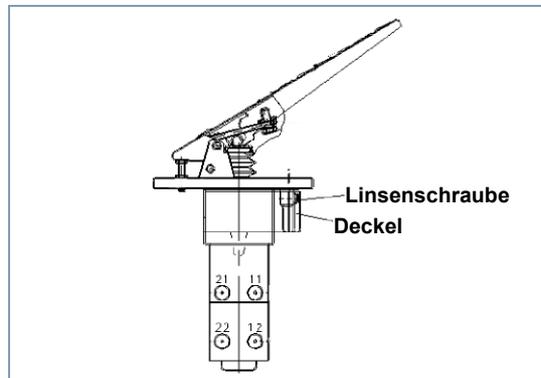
Motorwagen-Bremsventil 461 318 ... 0
